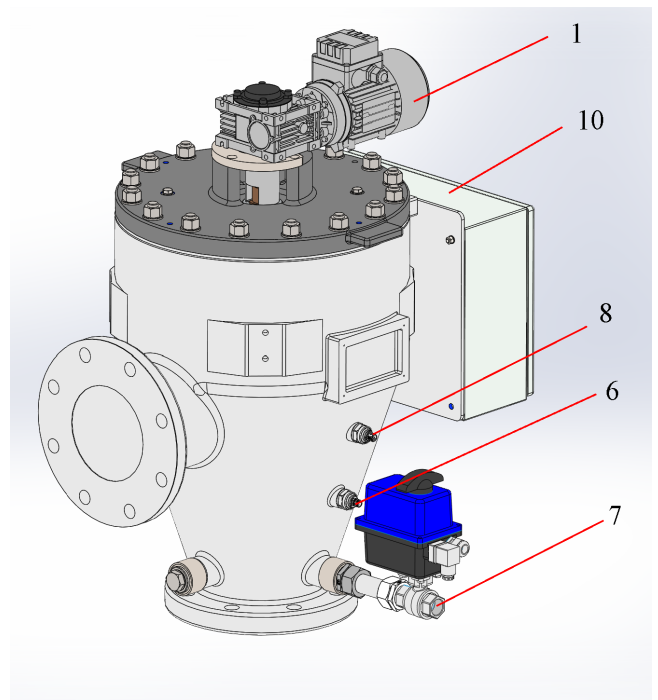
Bezeichnung der Hauptkomponenten R8-80
